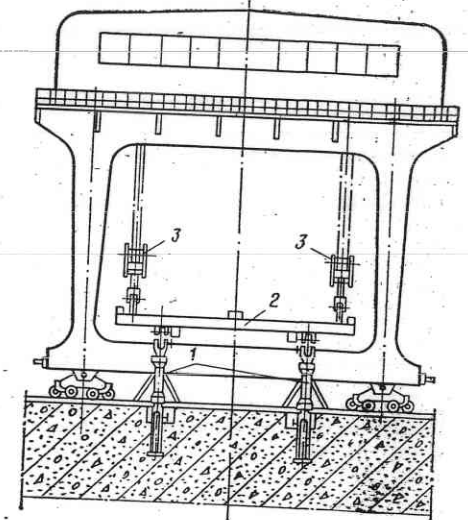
Схема испытания козлового крана гидродинамометрами
